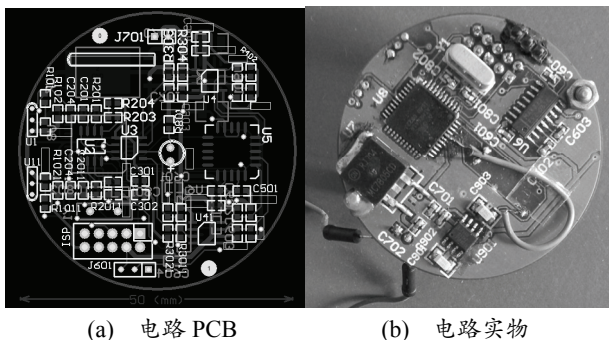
激光脉冲频率和能量测量电路 PCB 及实物对照
